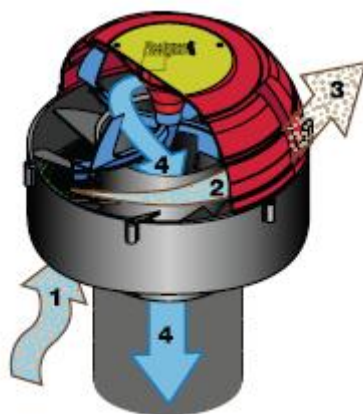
Vista 3D com corte do pré-filtro externo de ar Feetguard Sy-Klone da Cummins
